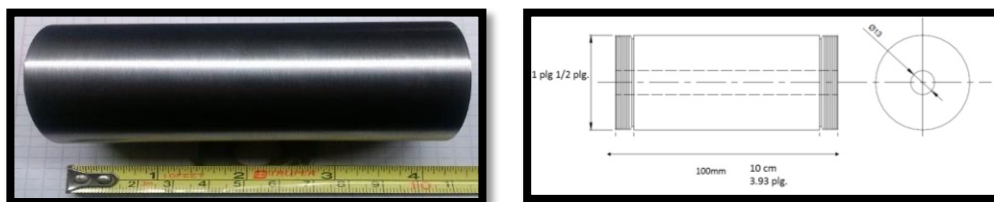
Probeta para ensayo de fatiga térmica. Derecha Dimensión para maquinado para la probeta de fatiga térmica
